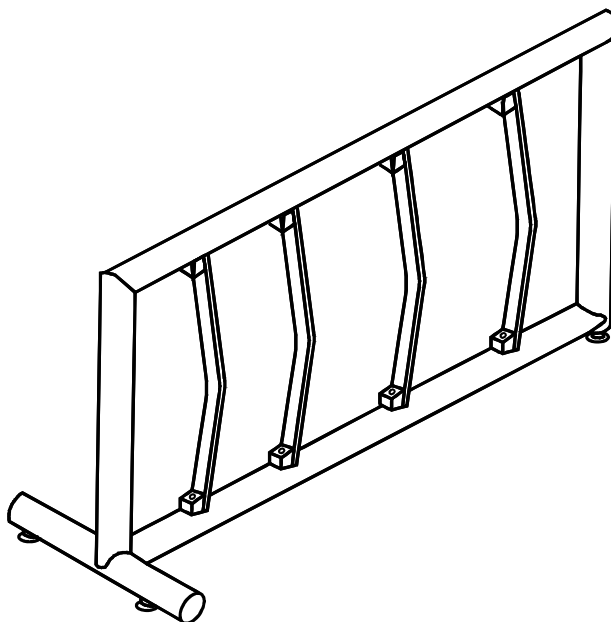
Сварное сборочное приспособление рамного типа на трех опорах
